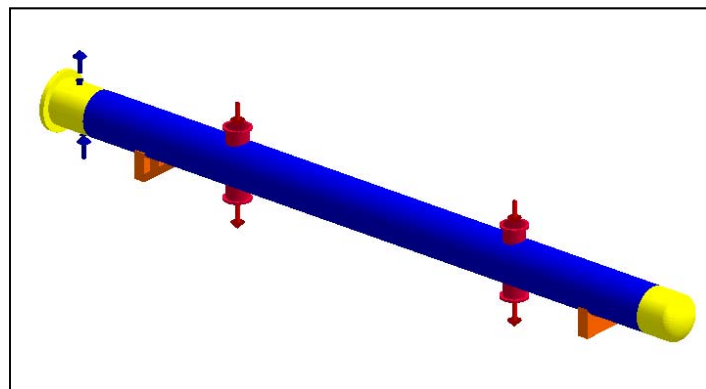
Imagen exterior del intercambiador Precalentador. Fuente: HTRI Output drawing.
